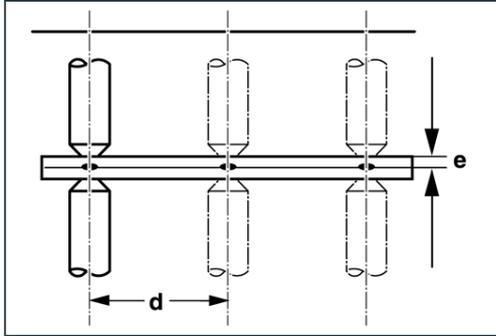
Relación grosor de chapa / distancia de los puntos de soldadura
